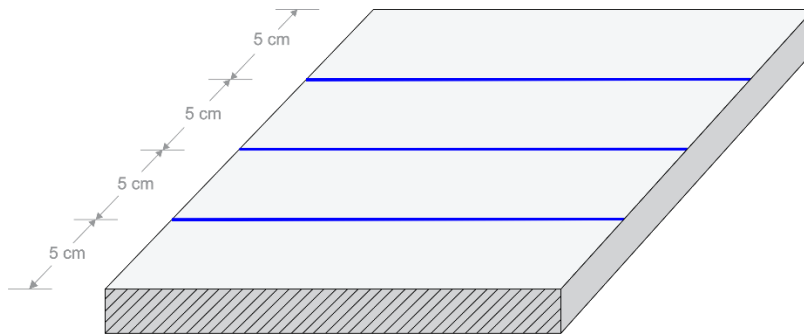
Esquemmatización de trazo de líneas guías para corte y soldadura con oxiacetileno.
